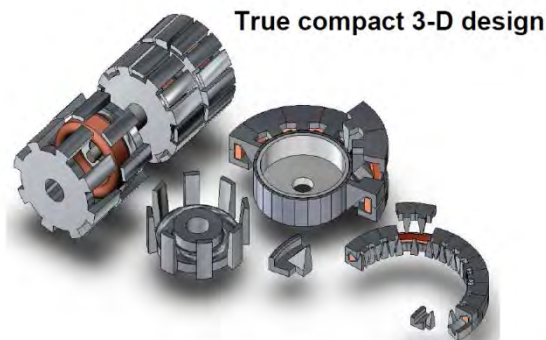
совершенствование конструкций двигателей за счет порошковых деталей, формирующих трехмерные магнитные потоки
